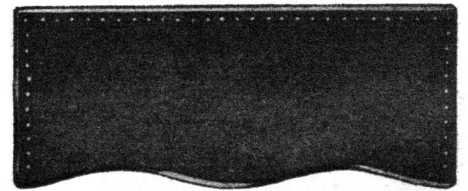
Abgewickelter Dampfdom, vor dem Umbördeln geschnitten.
